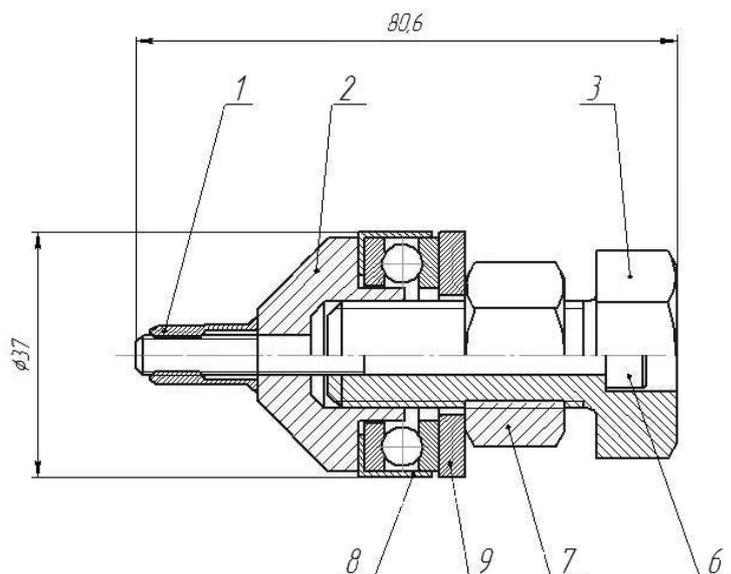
Общий вид устройства для монтажа резьбовых заклепок
